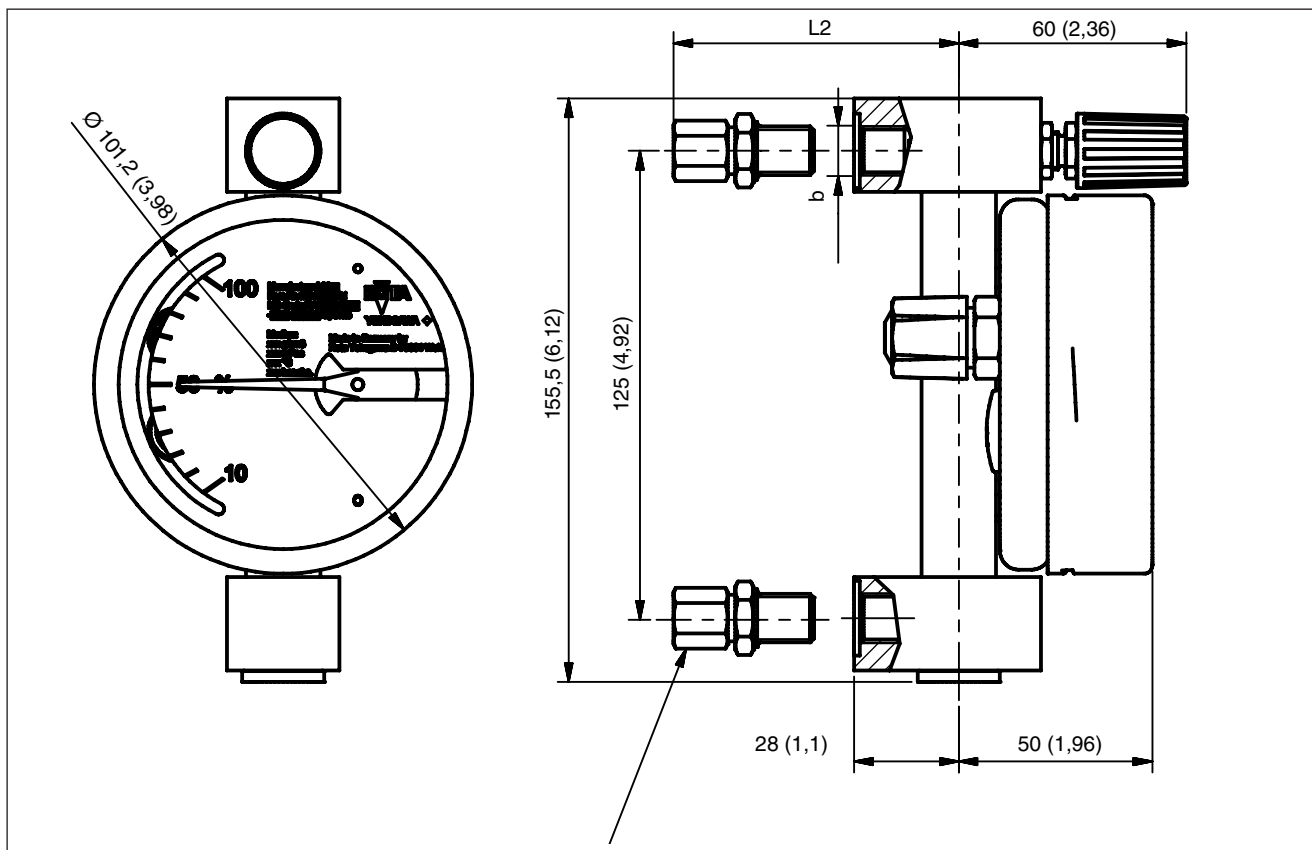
Ausführung mit Ventil im Ausgang, Abmessungen in mm (Zoll)
